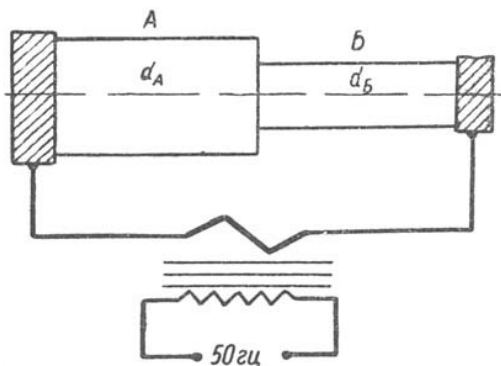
Схема подведения напряжения к заготовке с различным сечением
